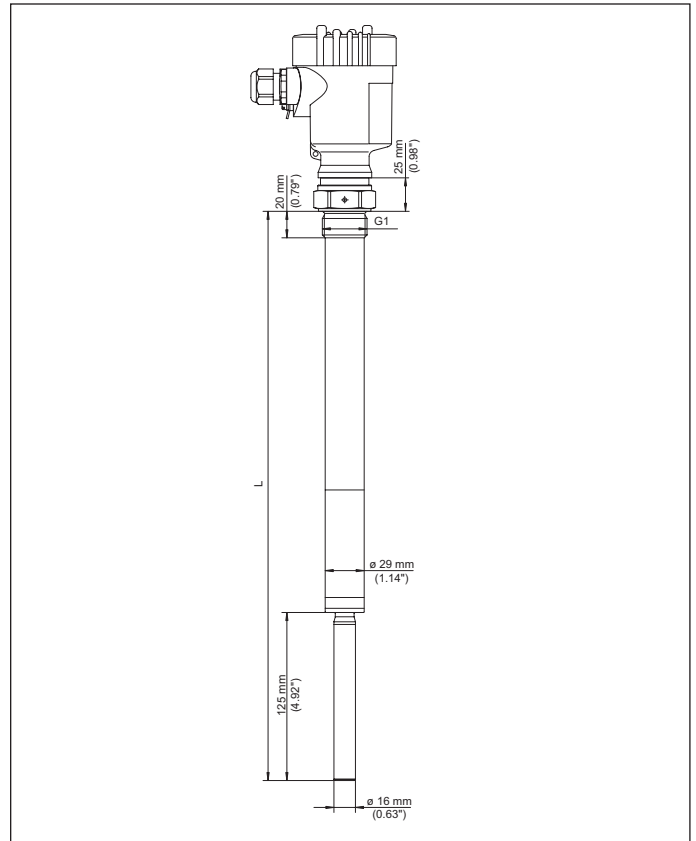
VEGAVIB 63 - Gewindeausführung G1
